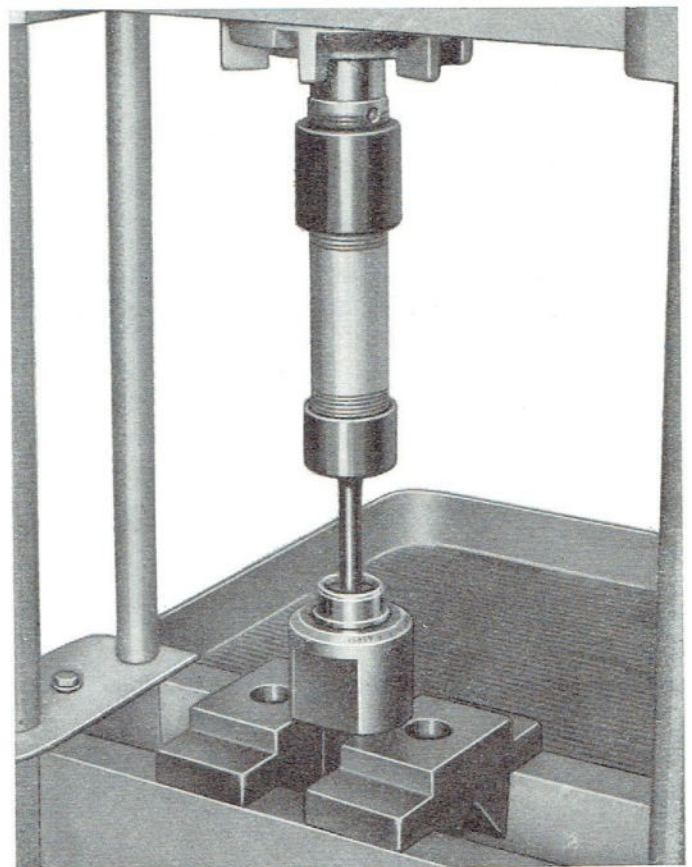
Abziehen des Innenrings des Rollenlagers für die Vorgelegewelle mit der Presse M. 1033 nach Anbringen des Werkzeuges A. 45031.
